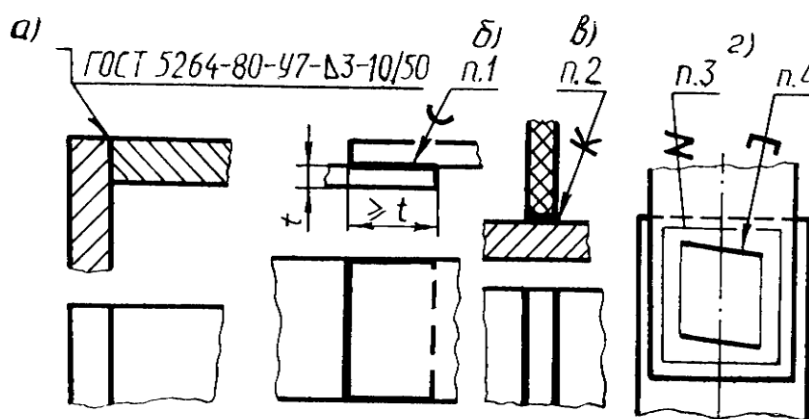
Условности при изображении швов соединений: а – сварного, б – паяного, в – клевого, г – сшивкой и скобками
